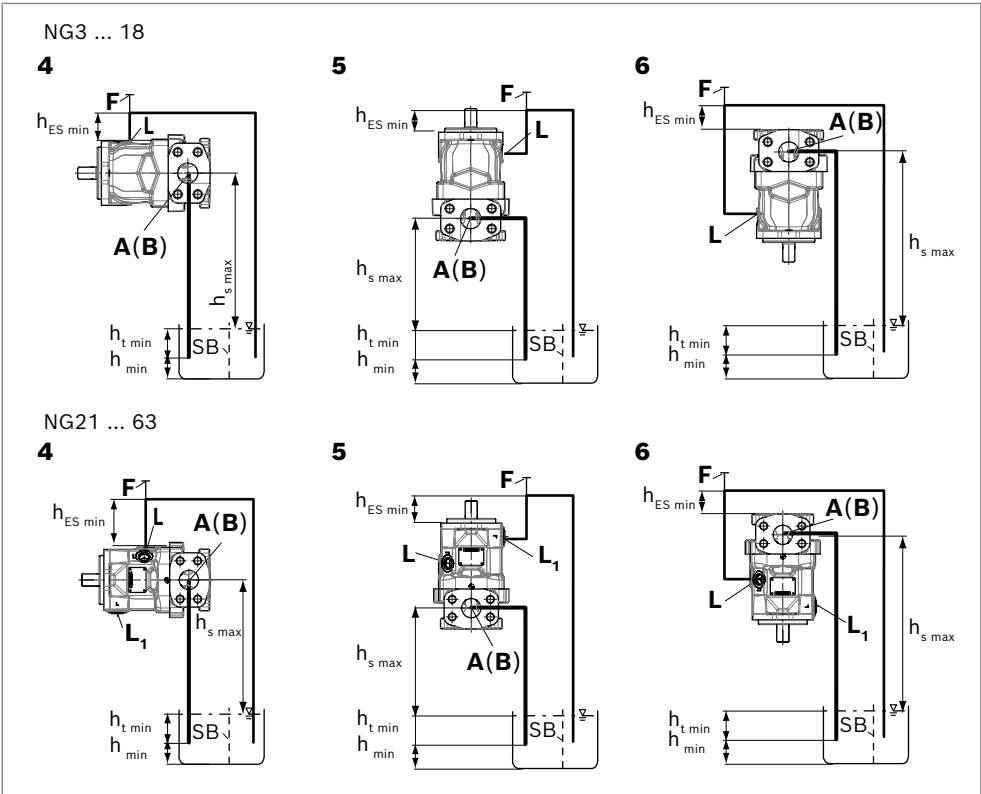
Übertankeinbau A10FZG mit Einbaulage 4–6
